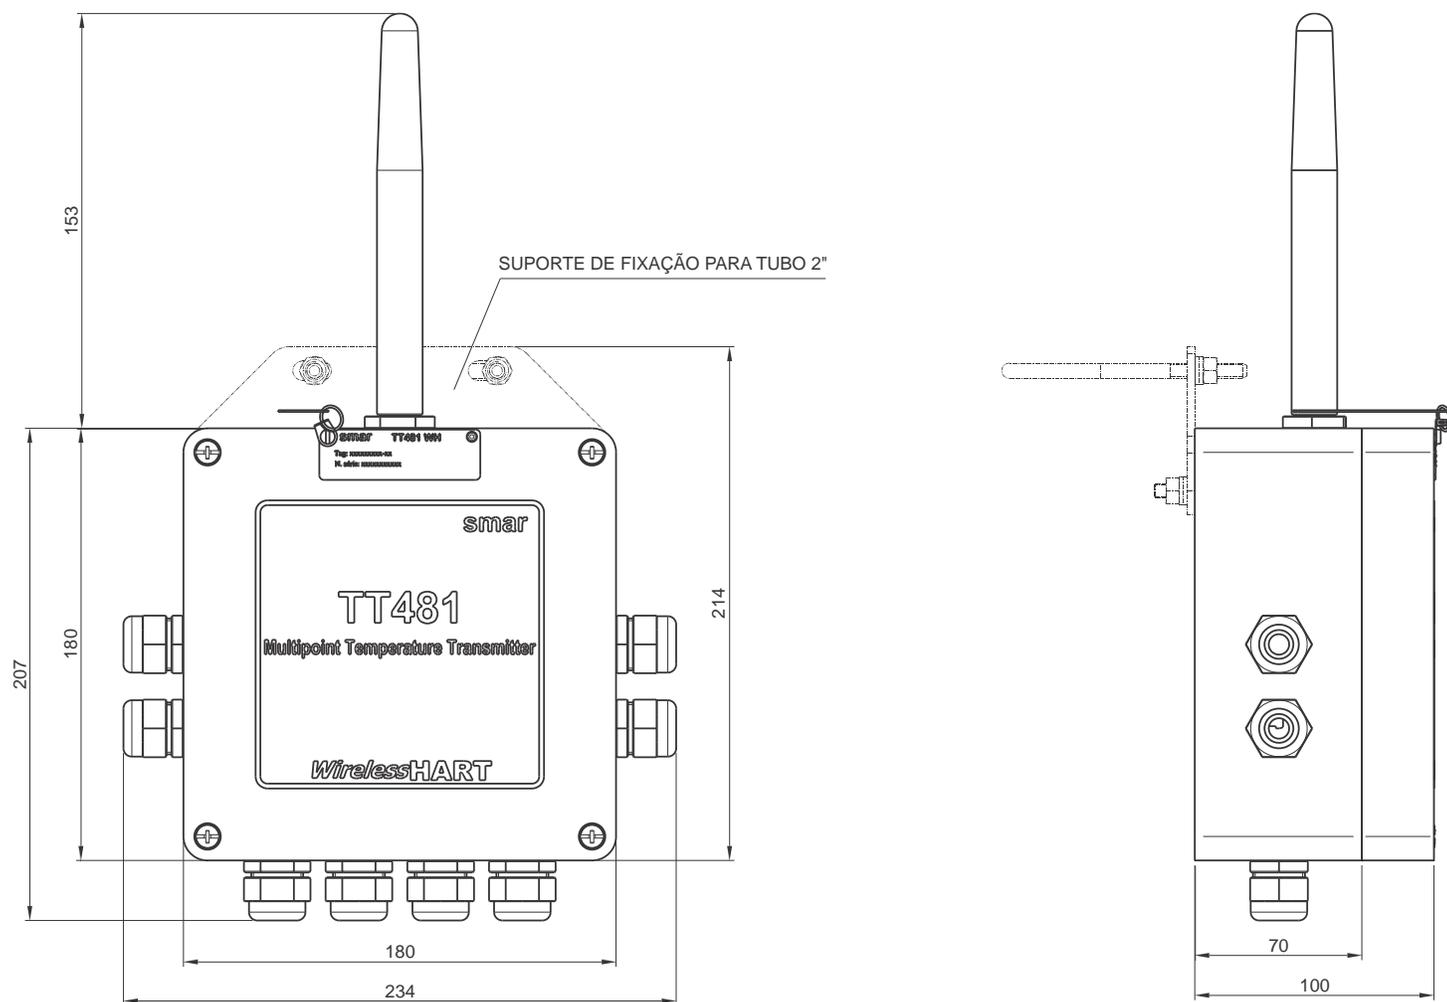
(b) - Desenho Dimensional - TT481 WirelessHART™ com 8 Canais
